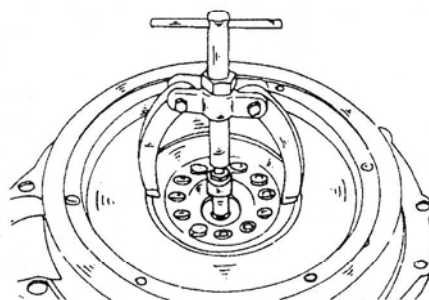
Снятие шарикового подшипника с коленчатого вала. Маховик должен оставаться закрепленным.
